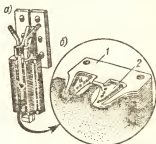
Индуктор с магнитопроводом для закали боковых поверхностей зубьев шестерен большого модуля: а — общий вид индуктора; б — эскиз поперечного сечения индуктора с закаленной шестерней:
